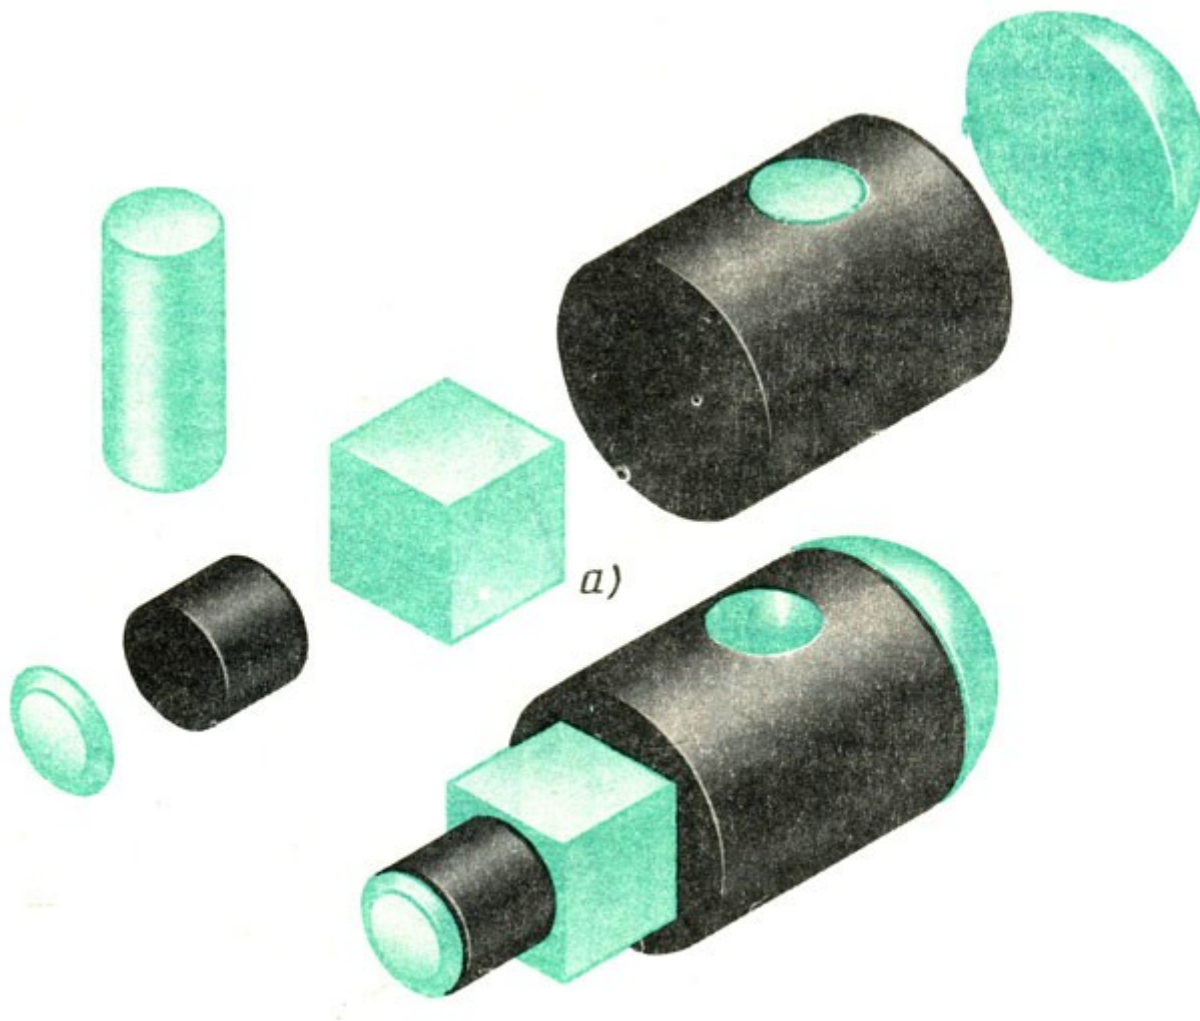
Анализ геометрической формы заготовки ключа: а - элементы детали; б - общий вид детали
